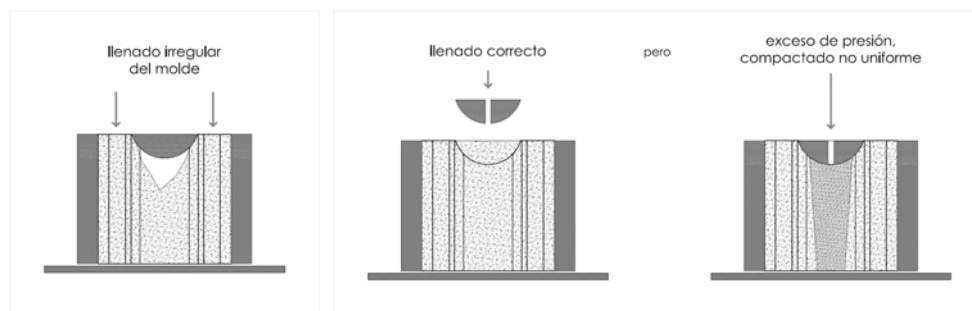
Posible llenado del molde irregular y defecto de compactado producido por las piezas soldadas en los corazones [izquierda]. Posible compactado no uniforme, con exceso de presión bajo los rebajes [centro y derecha].
